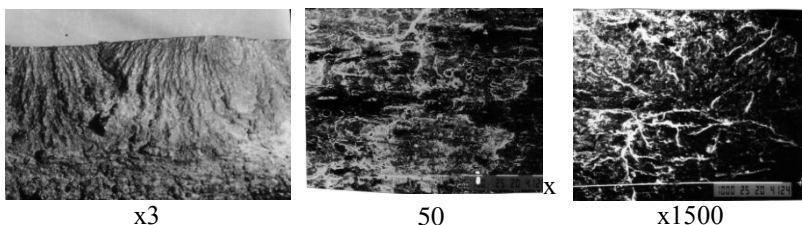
Поверхность излома в очаге разрушения: а — внешний вид поверхности; б — складчатый рельеф излома вблизи начала разрушения; в — грубые усталостные бороздки
